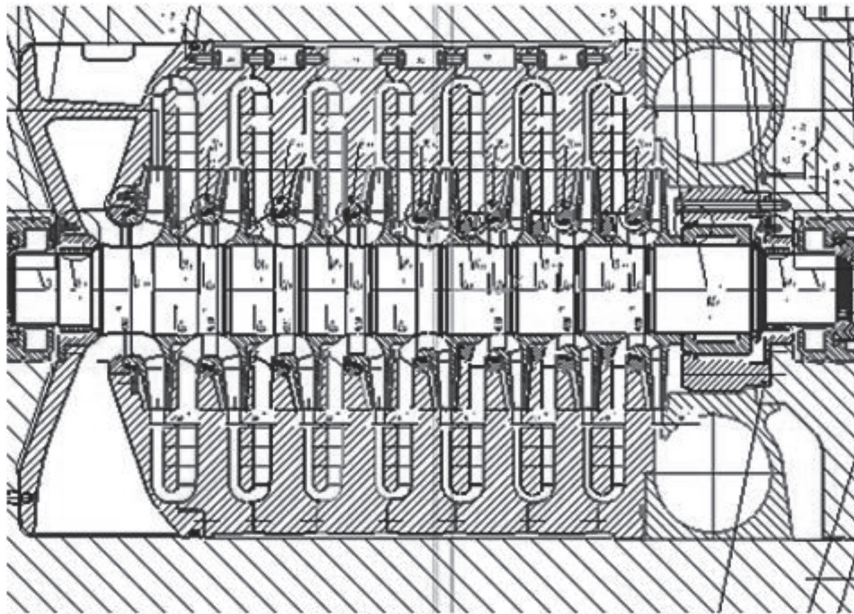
Общий вид конструкции центробежного компрессора ДКС
